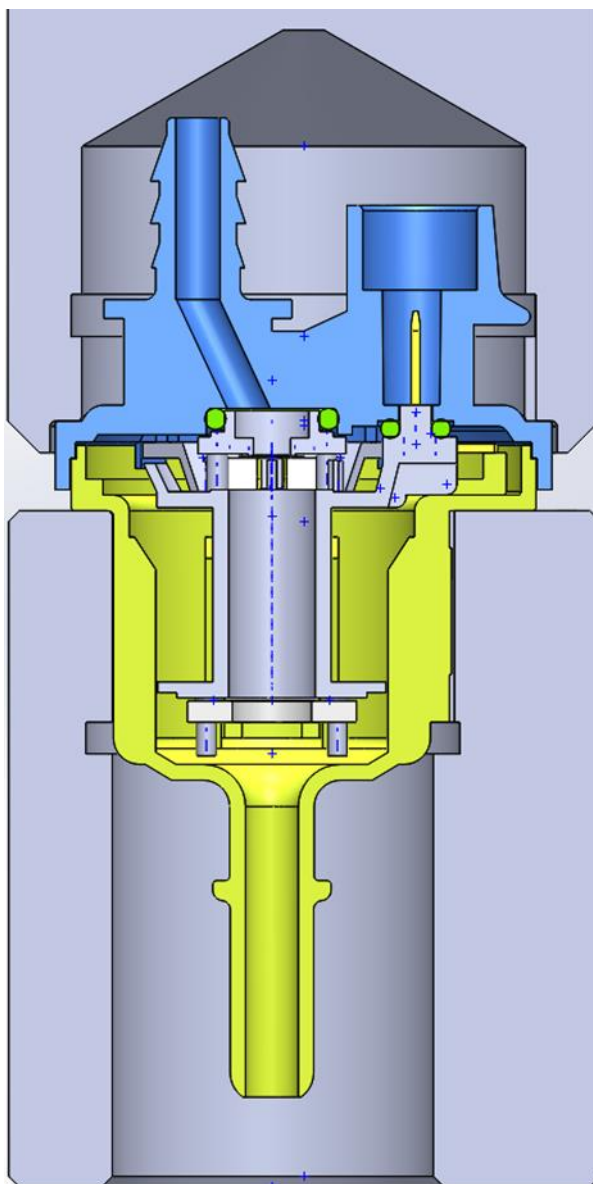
Расположение волновода и деталей в момент сварки
